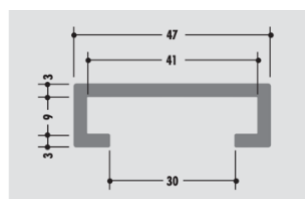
Sección de perfil en C, de plástico extruido. Fuente: (Röchling Industrial, 2018)
